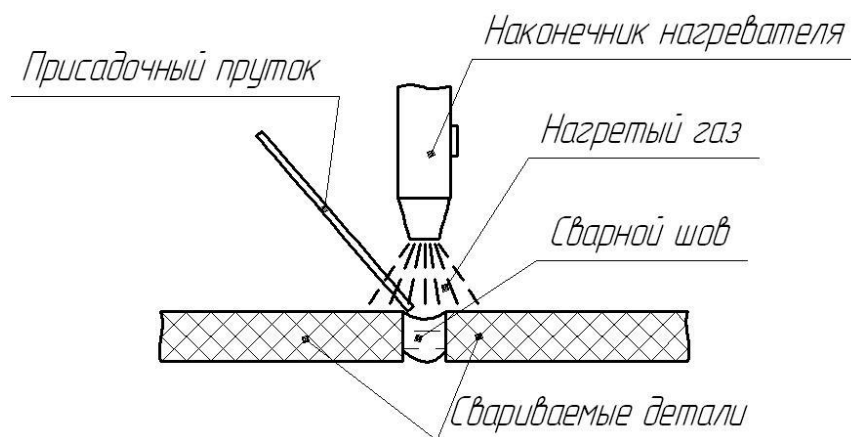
Сварка нагретым газом с применением присадочного материала
